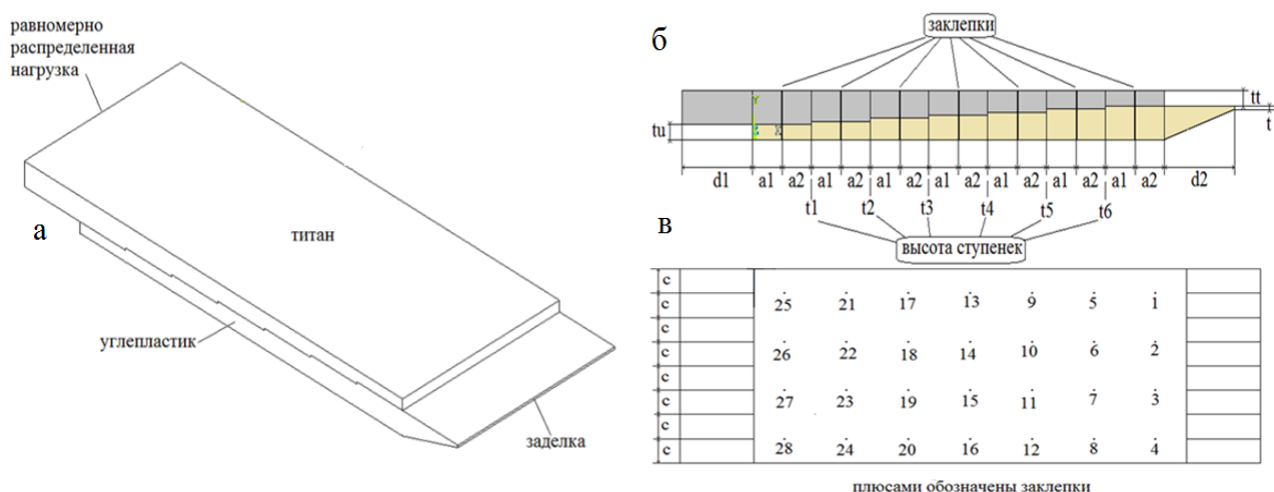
Схематичное изображение фиттинг-соединения – а; вид сбоку – б; вид сверху – в
